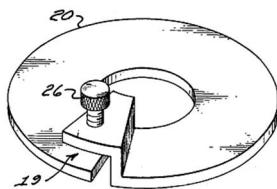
Общий вид вторичной катушки: 19 – воздушный промежуток; 20 – вторичная катушка; 26 – регулировочный винт
